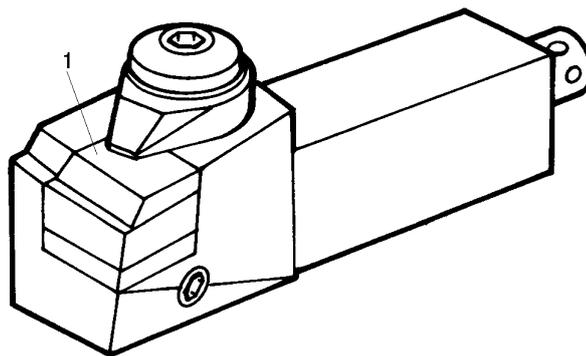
Сборный резец с механическим креплением пластины 1
